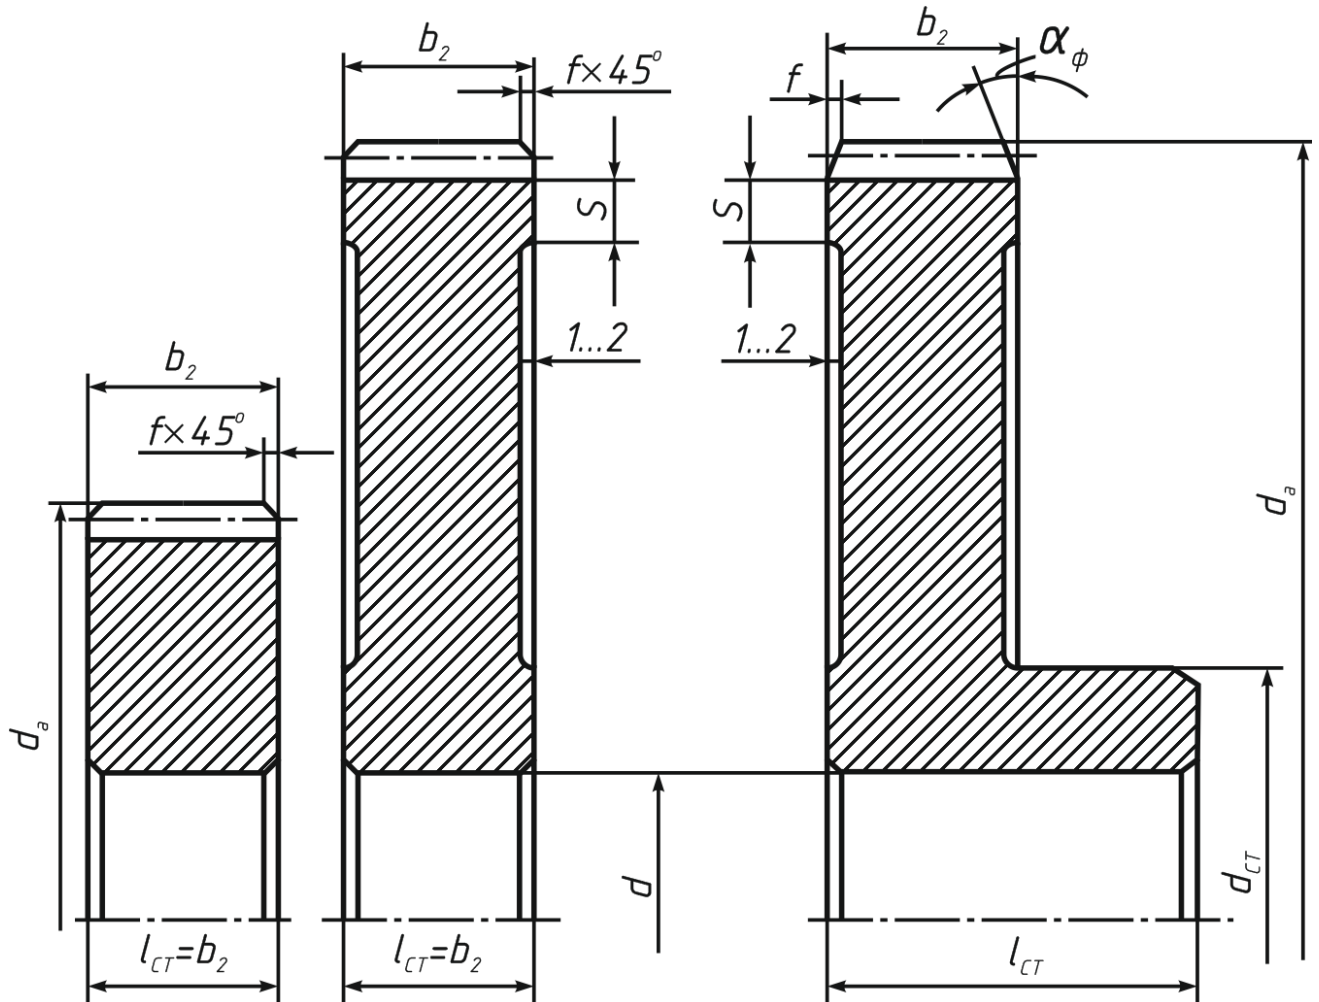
Основные геометрические параметры цилиндрического колеса внешнего зацепления
